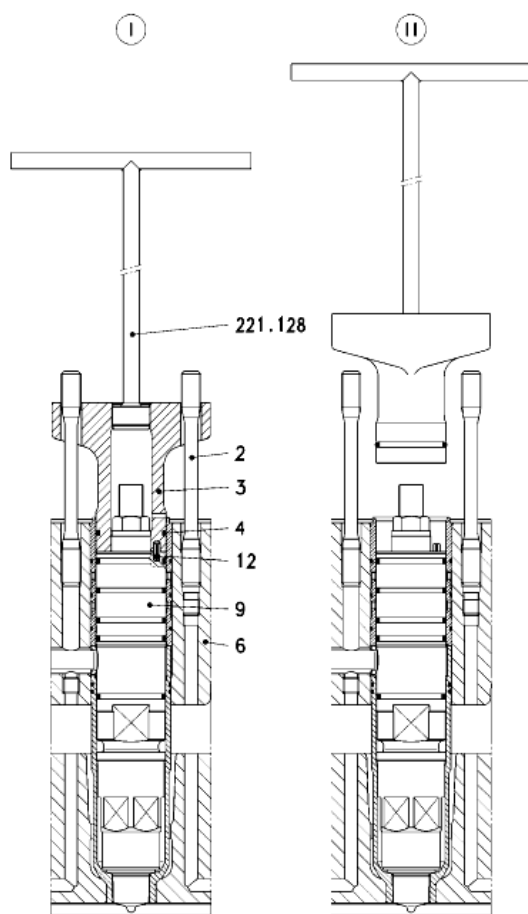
Зняття / встановлення тяги фланця: 2 – шпилька; 3 - упорний фланець; 4 - О-подібне кільце ущільнення; 6 - головка циліндра; 9 – паливна форсунка; 12 – штифт; I-II - робочі кроки
